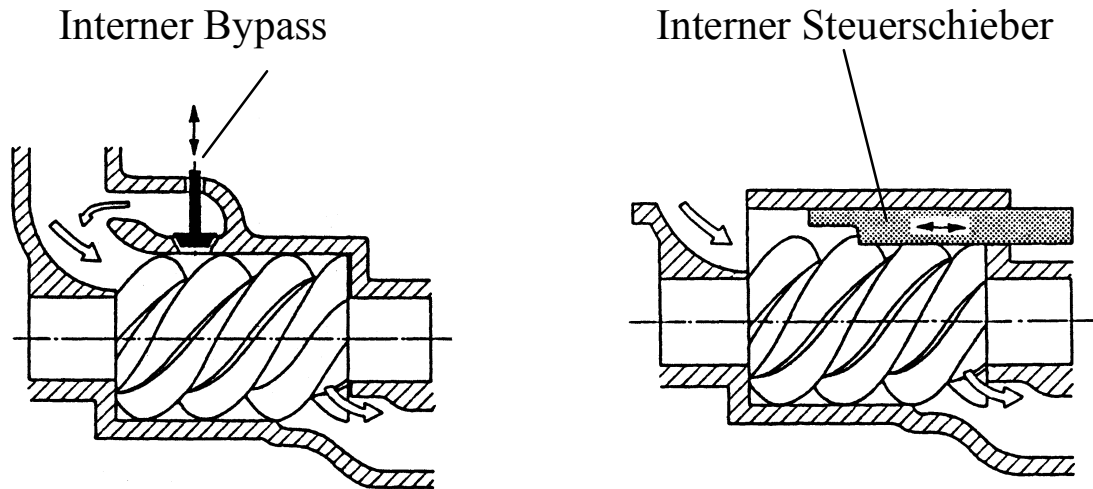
Ladedrucksteuerungskonzepte mit internen Steuerorganen für Schraubenlader [74]
